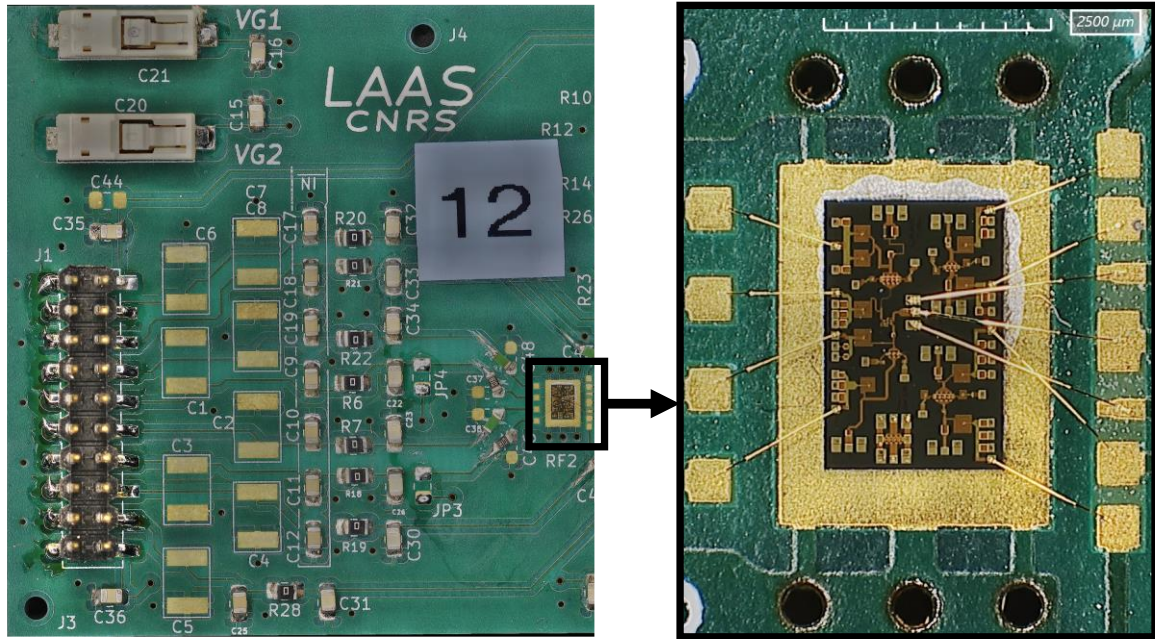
vue partielle du PCB, relative au circuit de découplage sur PCB / collage du MMIC sur PCB avec connexion par fils de bondings
